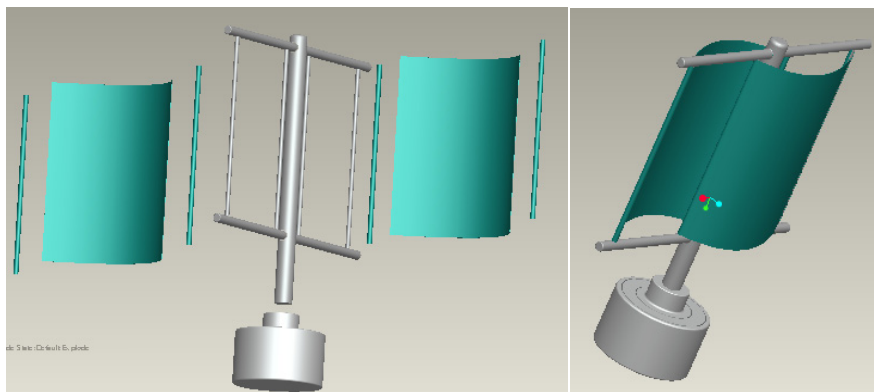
Φτερό α) Explode View, β)Unexploded View
